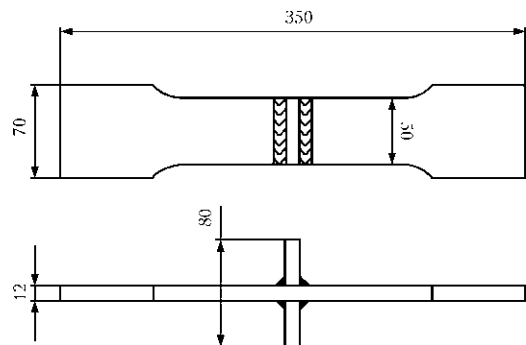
Схема образца сварного соединения стали 09Г2С
